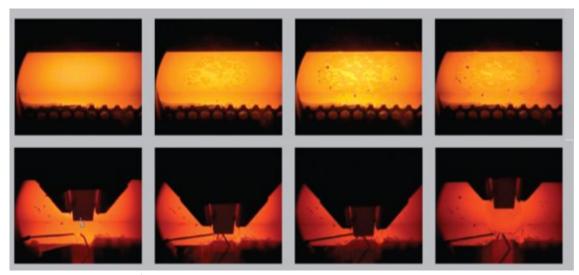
Образец, подвергаемый плавлению, затвердеванию и горячей деформации
